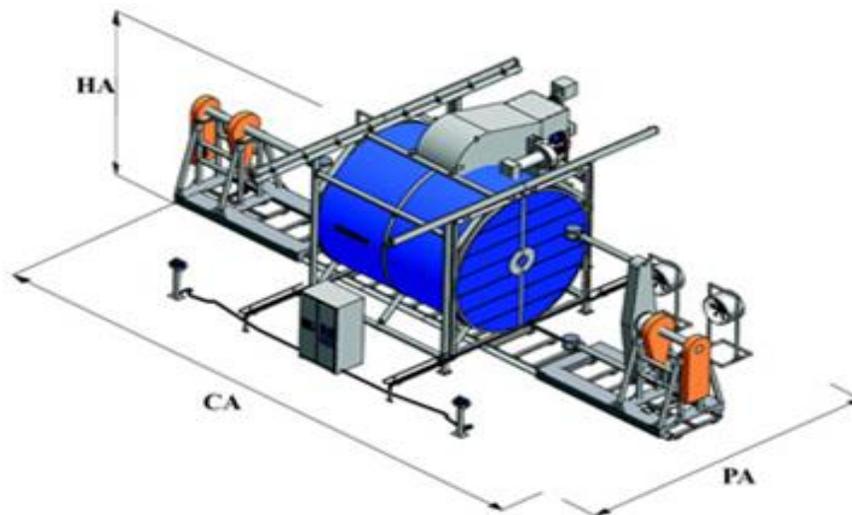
Máquina de rotomoldeo tipo shuttle. [62]
